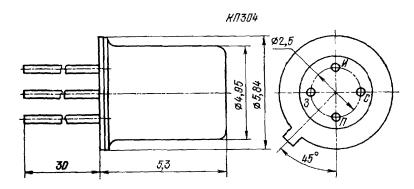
Габаритный чертеж для транзисторов КПЗО4А
